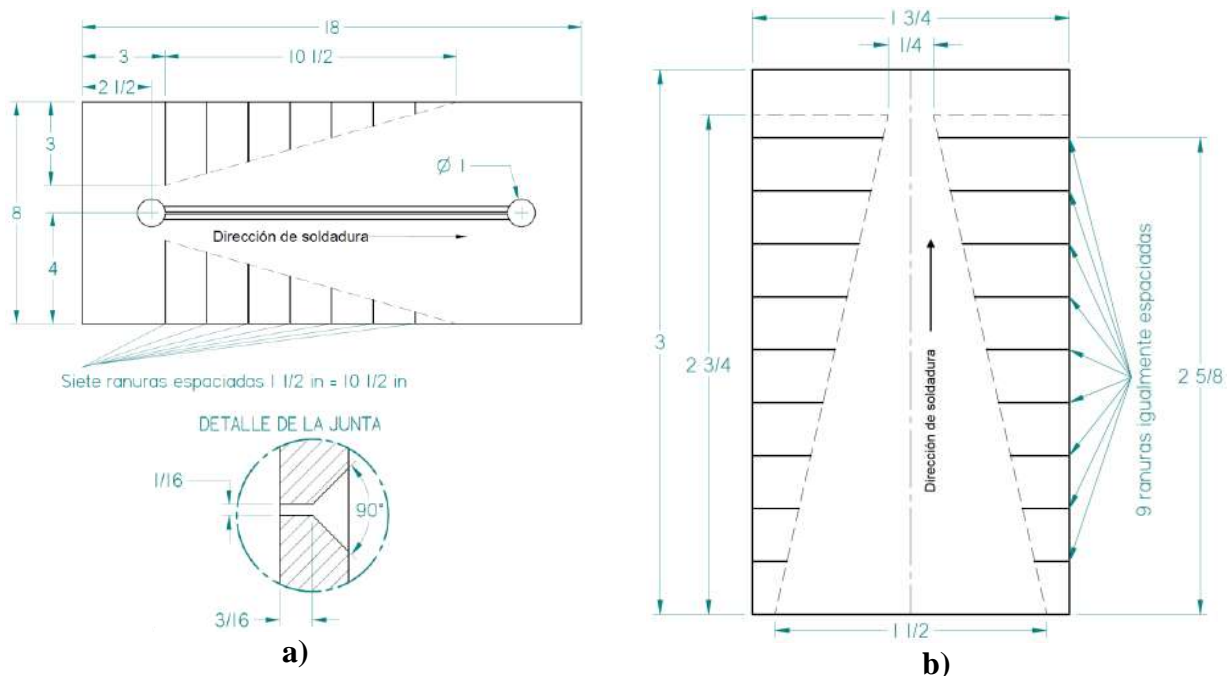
Dimensiones de las probetas de soldabilidad de a) Battelle modificado (espesor de 10 mm) y b) Houldcroft (espesor de 4 mm). Dimensiones en pulgadas
